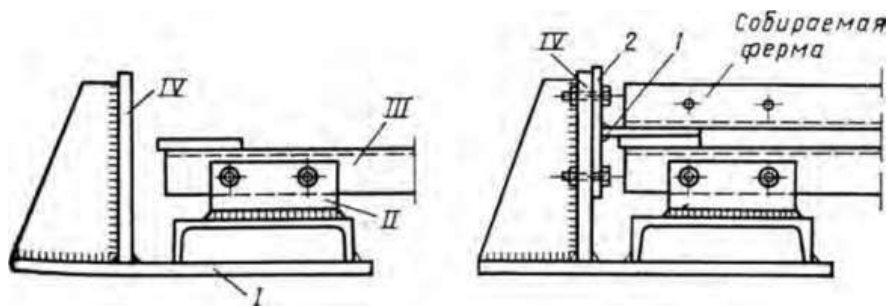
Копир с фиксатором для сборки стропильных ферм / — основание фиксатора; II — крепление фиксатора к копиру; III — копир; IV — стойка фиксатора предварительно сваренные с фасонками I. Их правильное положение обеспечивают совмещением монтажных отверстий концевых планок с отверстиями в стойке фиксатора 4. Затем на копиере раскладывают все остальные элементы, производят прихватку, ферму снимают с копира, кантуют и дособируют, как описано выше.
